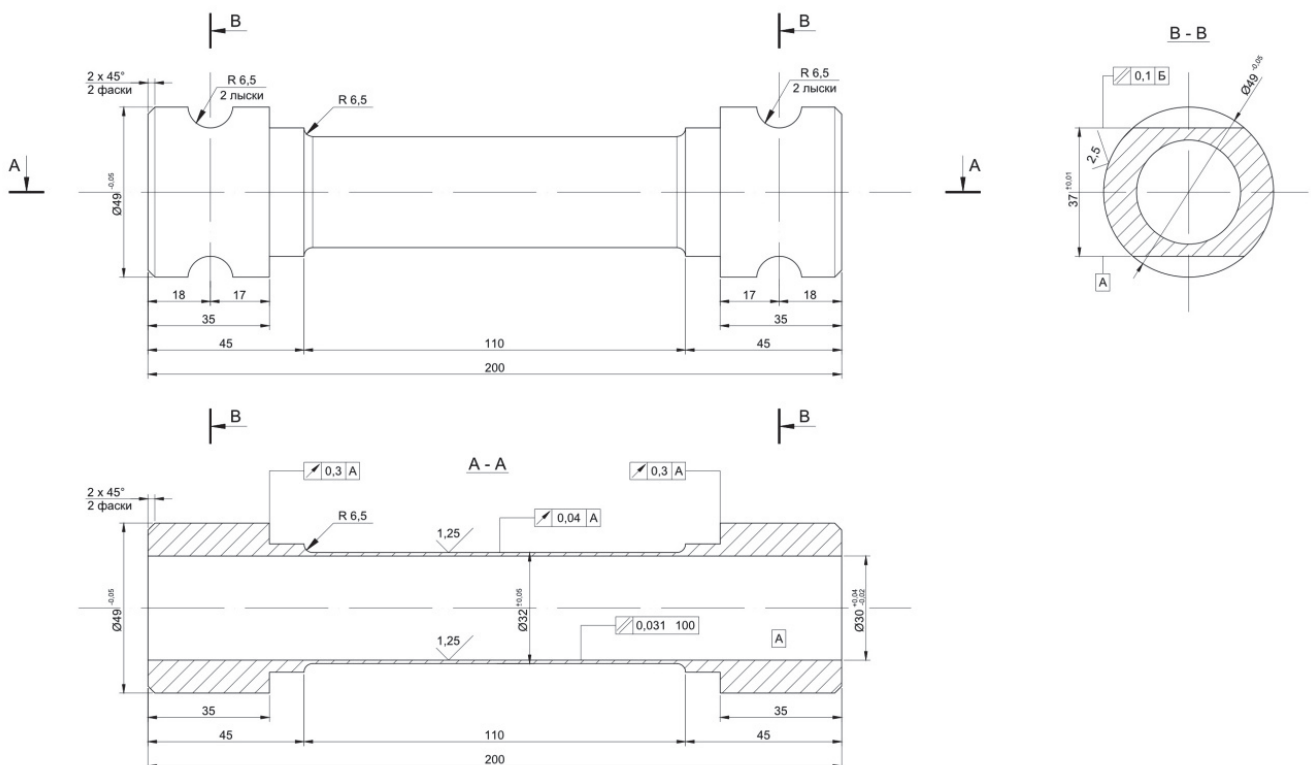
Чертеж образца цилиндрической оболочки для испытаний
